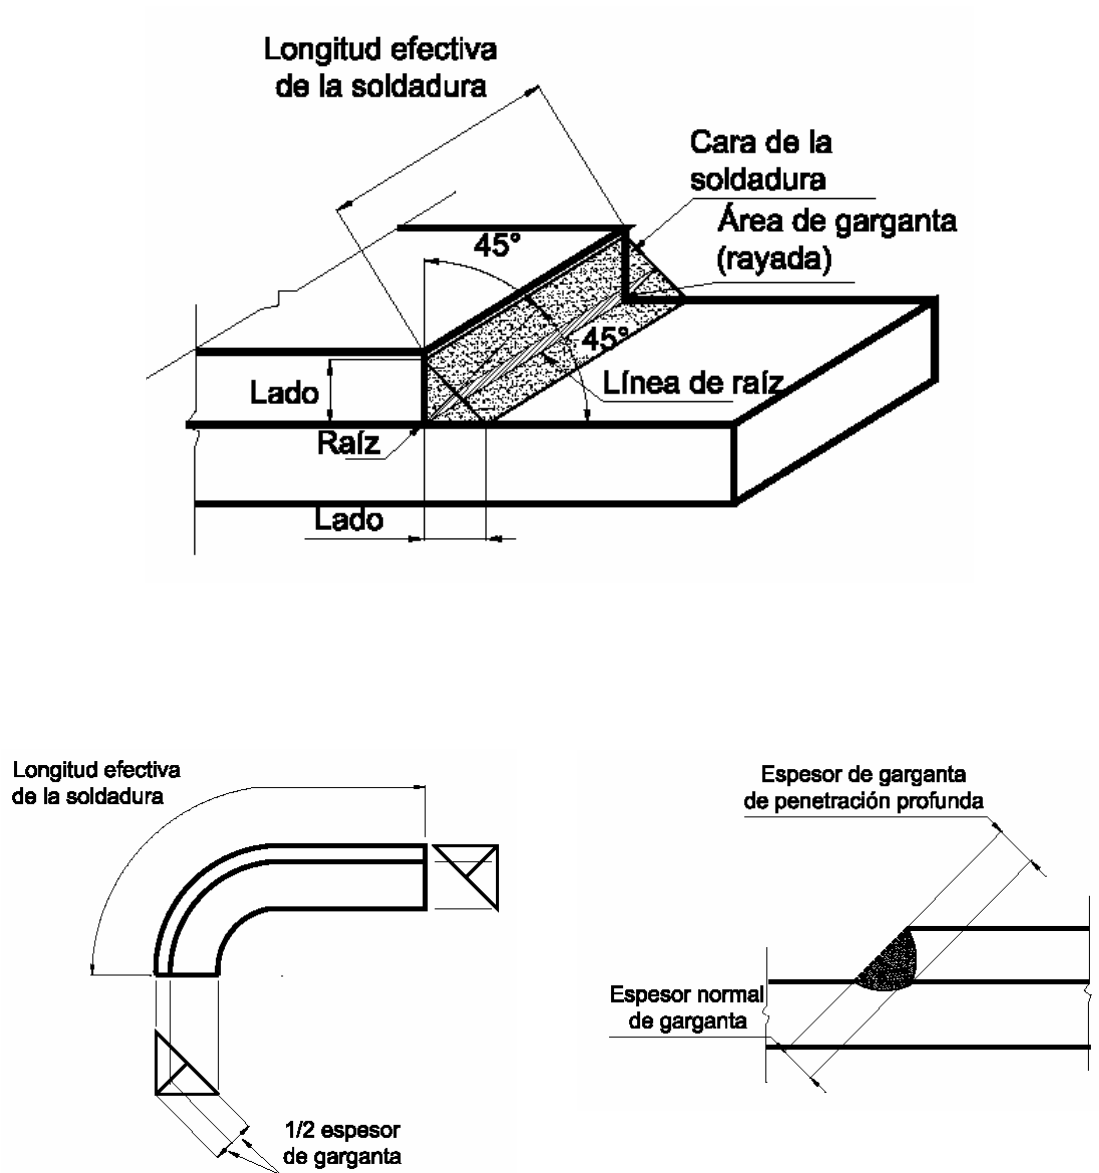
Nomenclatura de la soldadura según la AWS.
